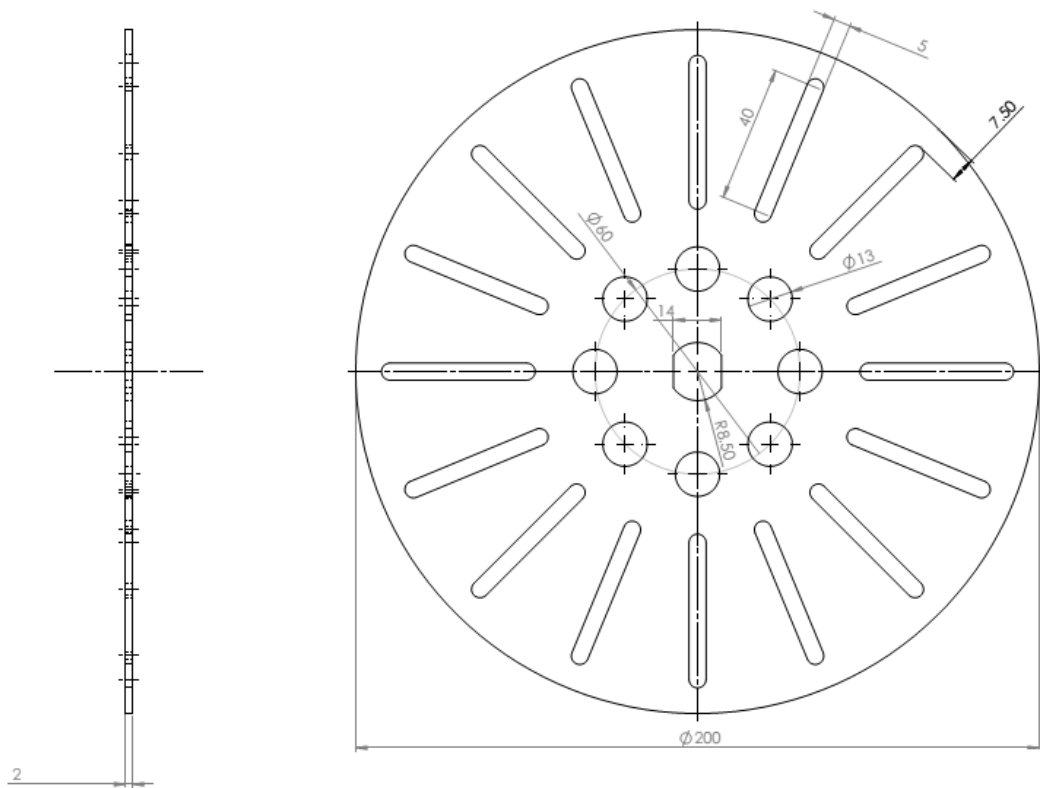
Dimensões (em milímetros) dos discos do rotor tipo H.
